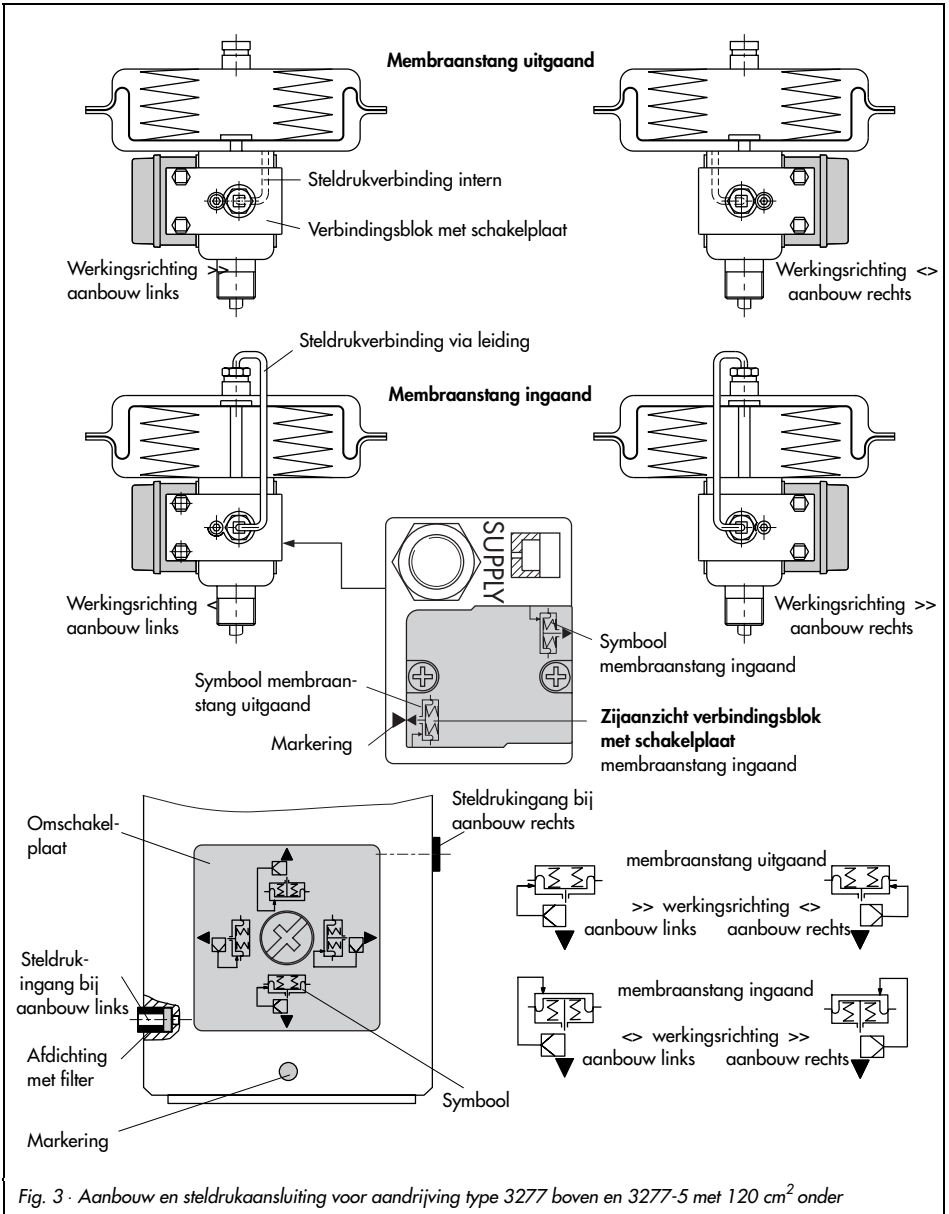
· Aanbouw en steldrukaansluiting voor aandrijving type 3277 boven en 3277-5 met 120 cm² onder
